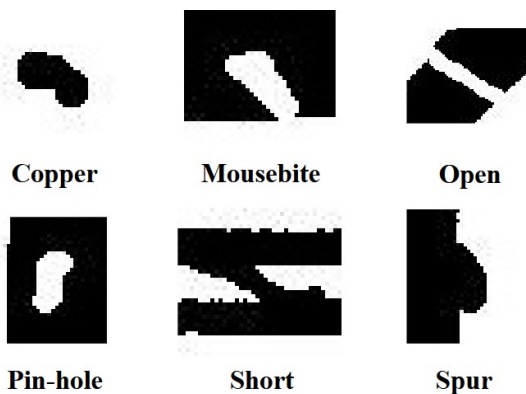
切割出來的 6 種 PCB 瑕疵區塊
